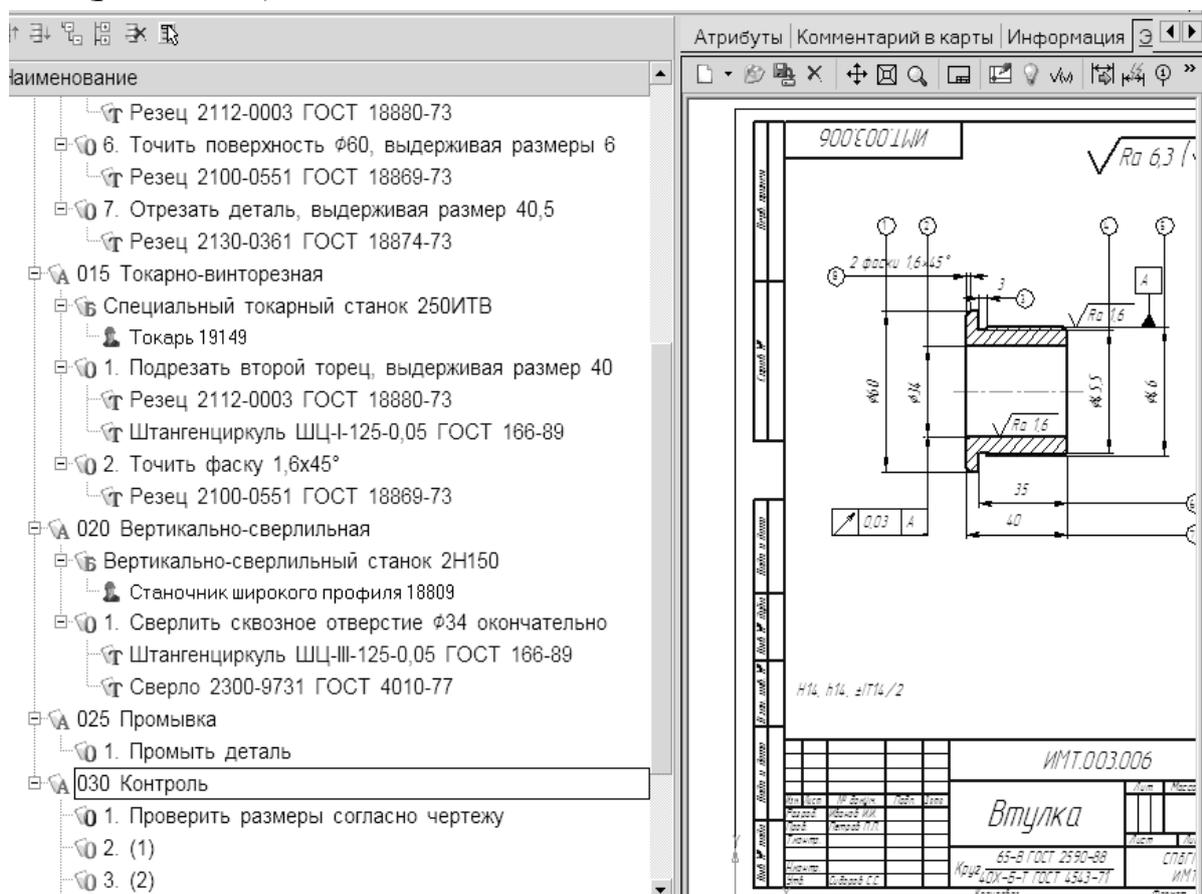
Проверка и маркировка размеров, согласно чертежу
